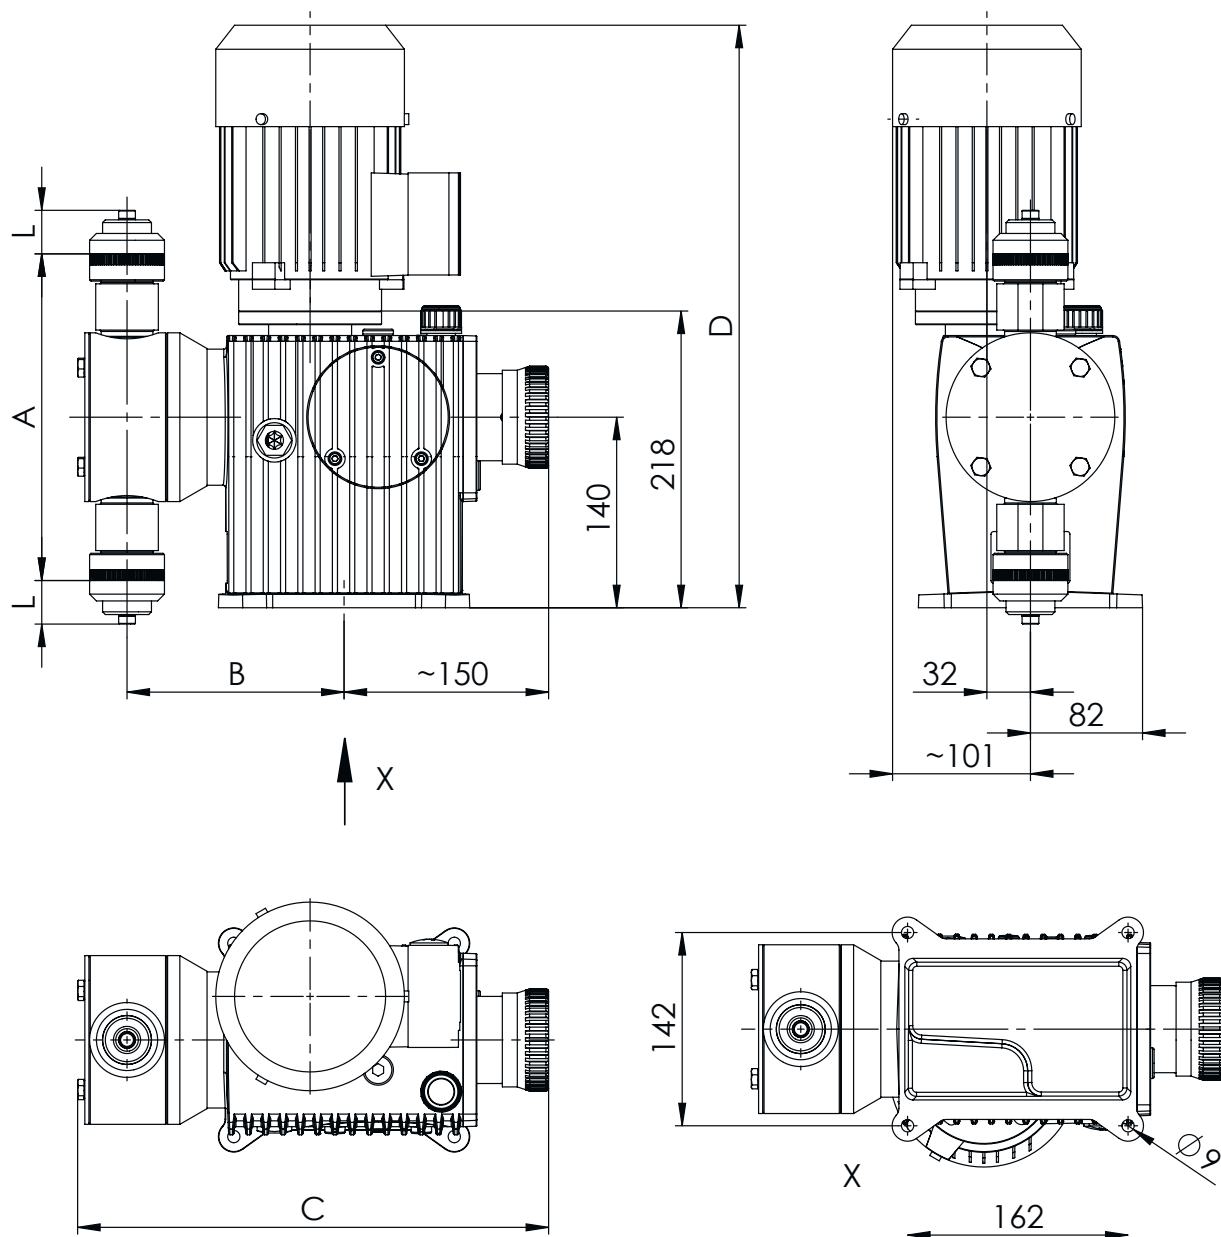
Габаритный чертеж MEMDOS LB 110, 160 – 1010
